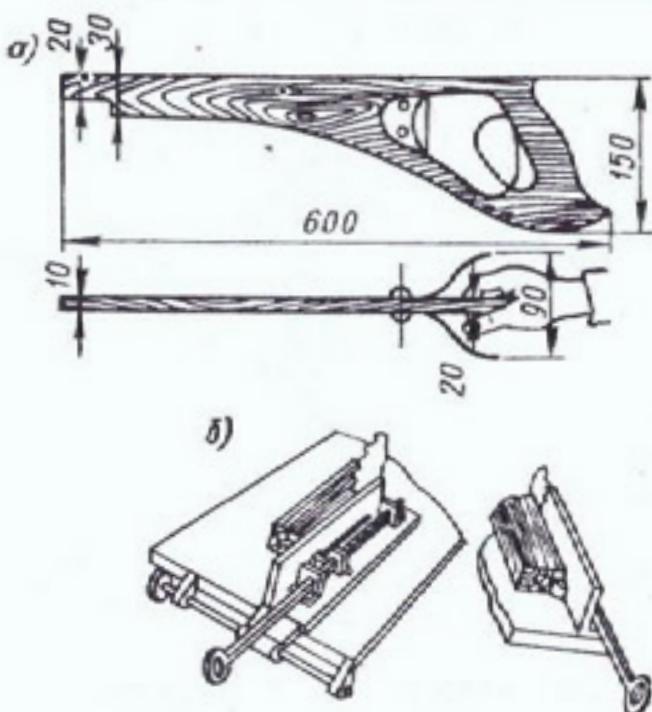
Предохранительные толкатели для допиливания заготовок на круглопильном станке: а — толкатель с металлическим предохранителем; б — толкатель, вмонтированный в направляющую линейку.
